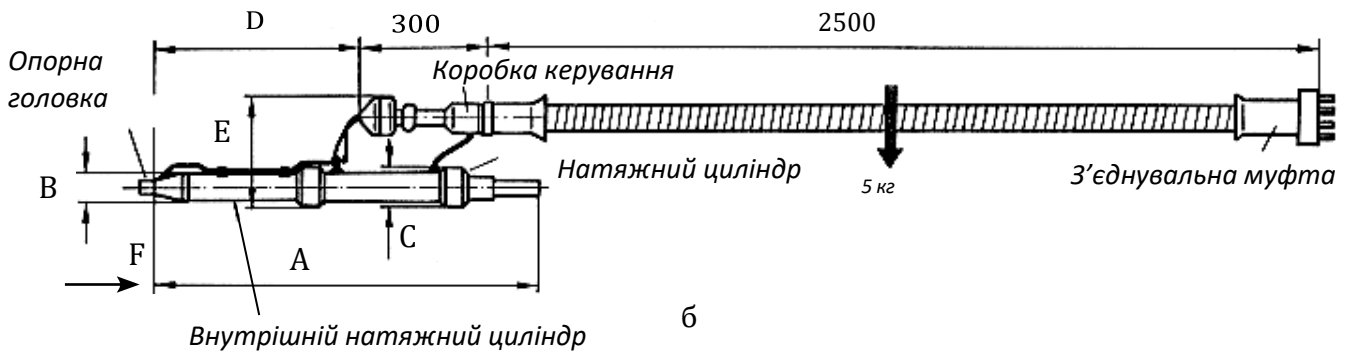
Загальний вигляд автоматичного однодротового натяжного домкрата (4-шлангова конструкція) фірми Paul і автоматичного насосного агрегату
